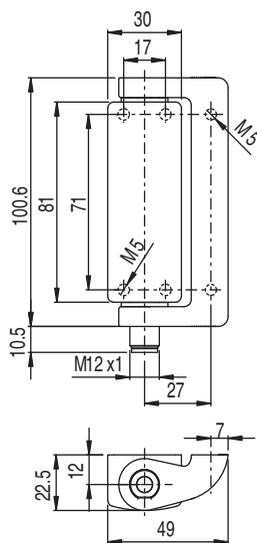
Dimensões do S400-M4M12-B em mm
